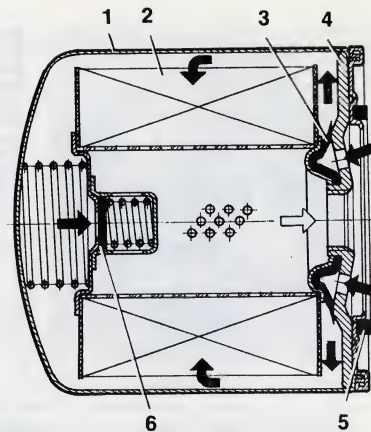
Устройство неразборного масляного фильтра ВАЗ модели «2101»: 1 — корпус; 2 — фильтрующий элемент; 3 — противодренажный клапан; 4 — дно корпуса; 5 — прокладка; 6 — перепускной клапан. Черными стрелками показан путь неочищенного масла, белой — отфильтрованного.
